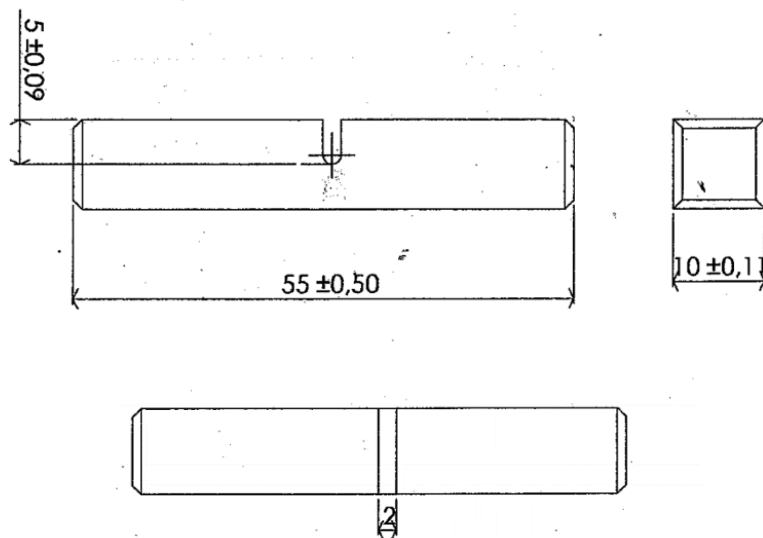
Dimensions d'une éprouvette de résilience (toutes les dimensions sont en mm).
